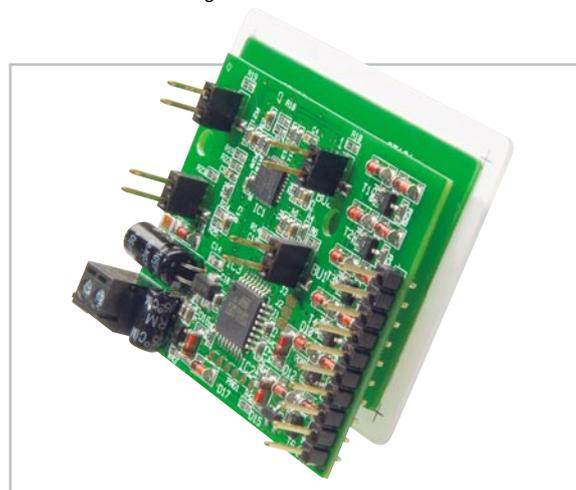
Komplett zusammengebaute Platinenkonstruktion
